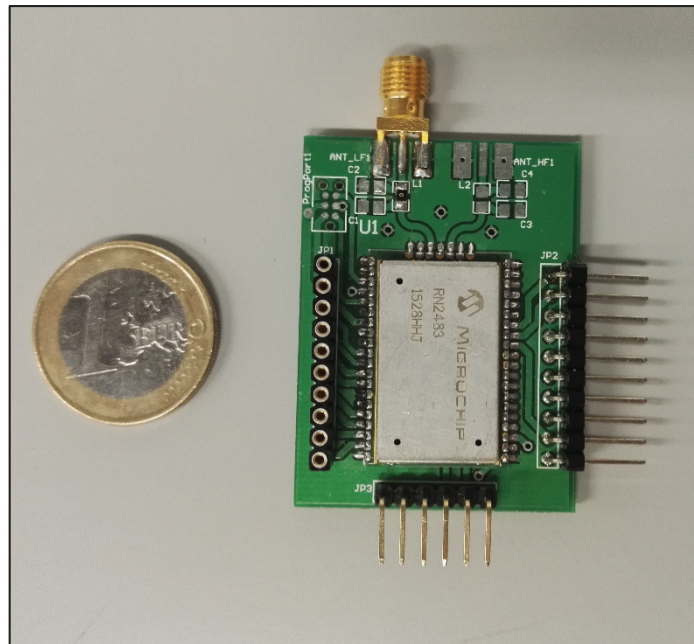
Módulo RN2483 montado sobre la PCB para pruebas LoRa.
